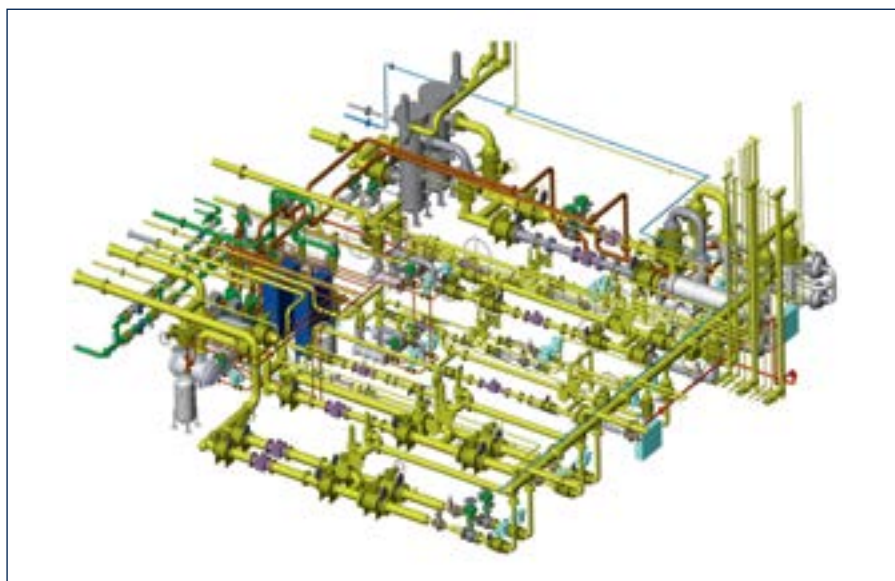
Сборочный чертеж многомодульной установки подготовки топливного газа «ЭНЕРГАЗ»
